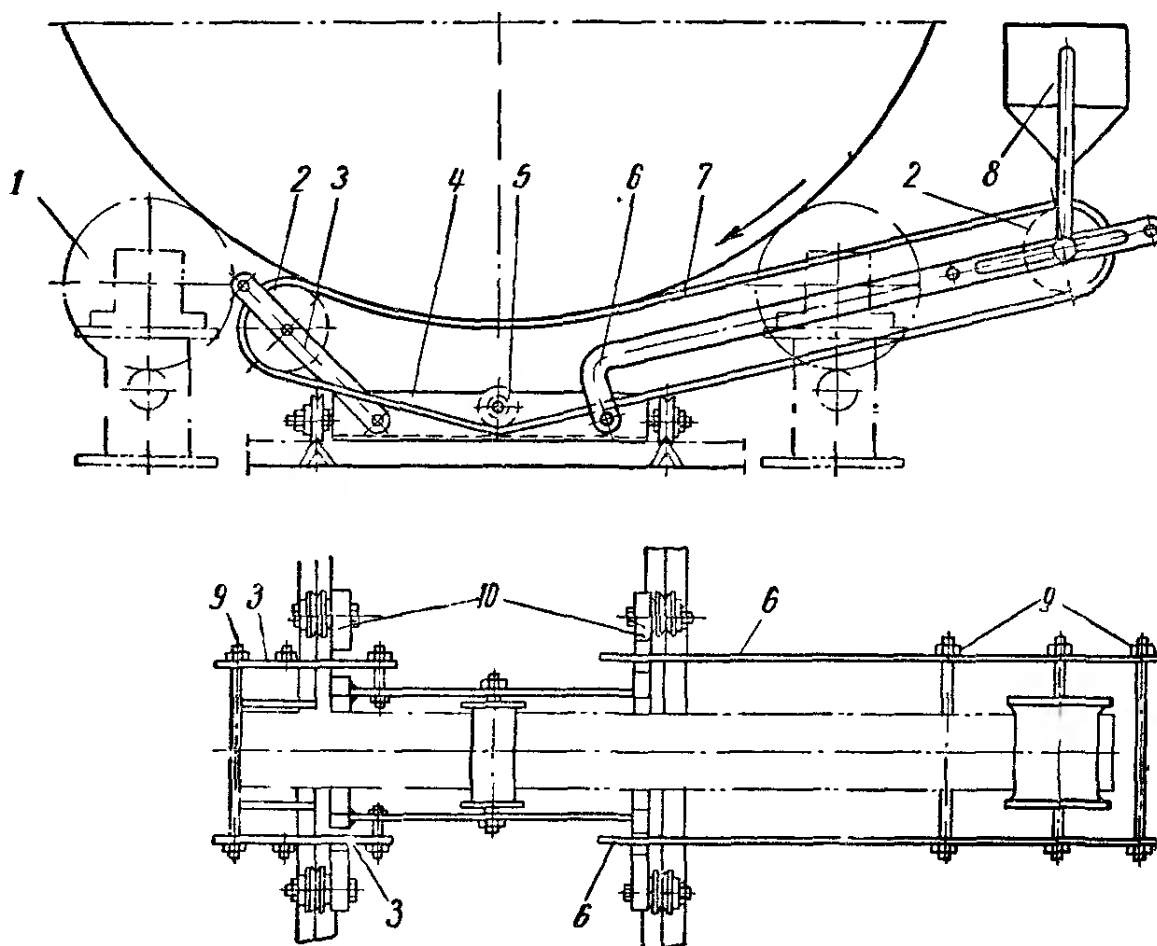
Схема устройства подвижной флюсовой подушки для сварки кольцевых швов резервуаров
